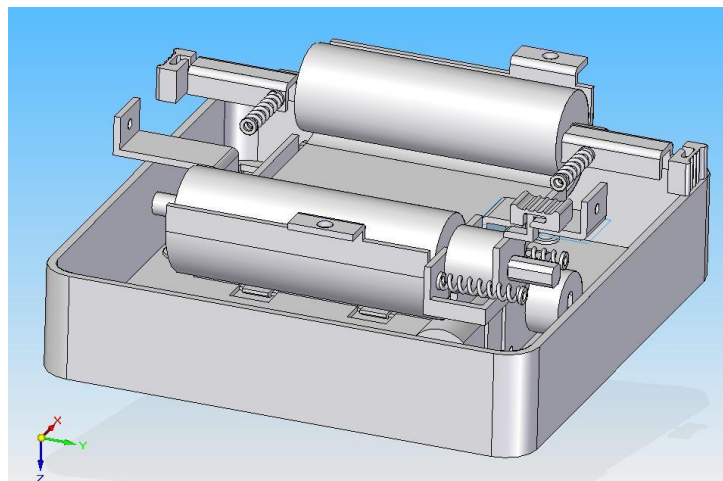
Etapa de transmisión para el rodillo sin la cubierta superior del encapsulado
